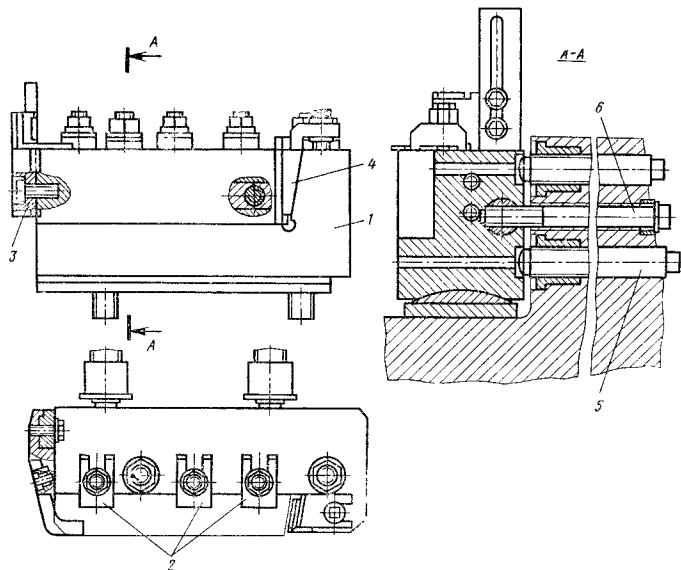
Плашкодержатель резьбонакатного автомата с плоскими плашками
